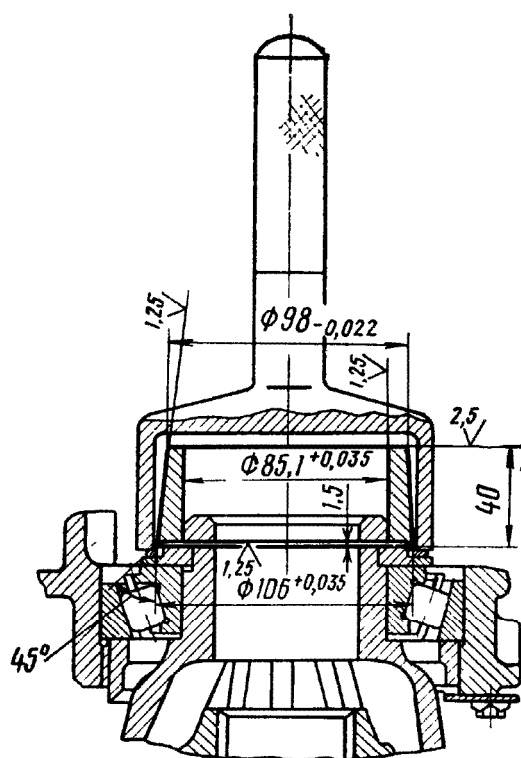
Оправка для установки кольца на сухарь подшипника чашки дифференциала
